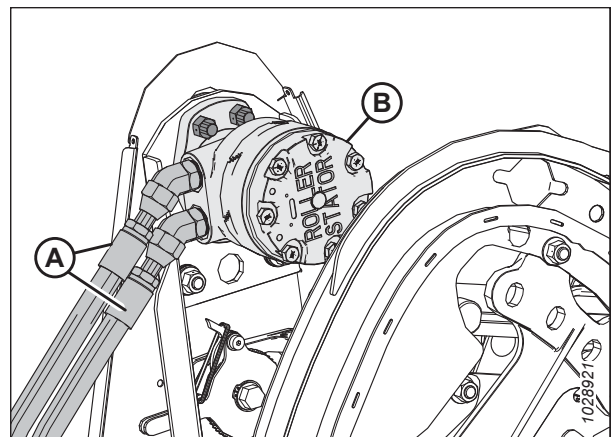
Haspelmotor und Hydraulikschläuche
